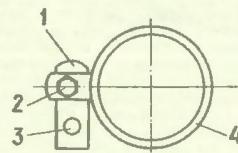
Крепление троса на рулевой колонке: 1 — дополнительная пластина; 2 — болт; 3 — отверстие для крепления троса; 4 — рулевая колонка.
